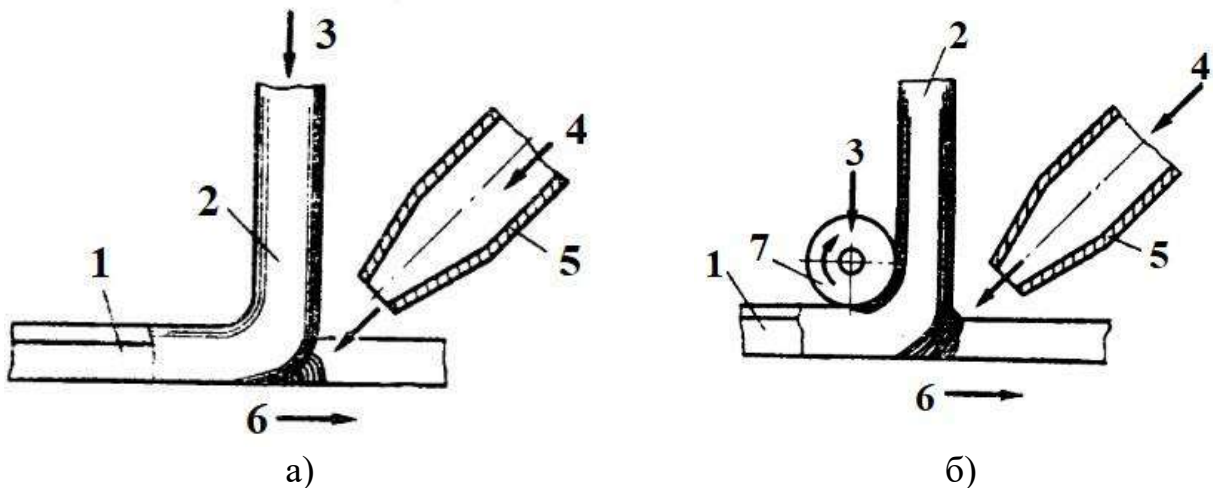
Зварювання нагрітим газом з присадним прутком (а) та прикочуванням (б): 1 – деталь, що зварюється; 2 - присадковий пруток; 3 – зусилля; 4 – нагрітий газ; 5 – сопло; 6 – напрямок зварювання; 7 – натискний ролик газу;
